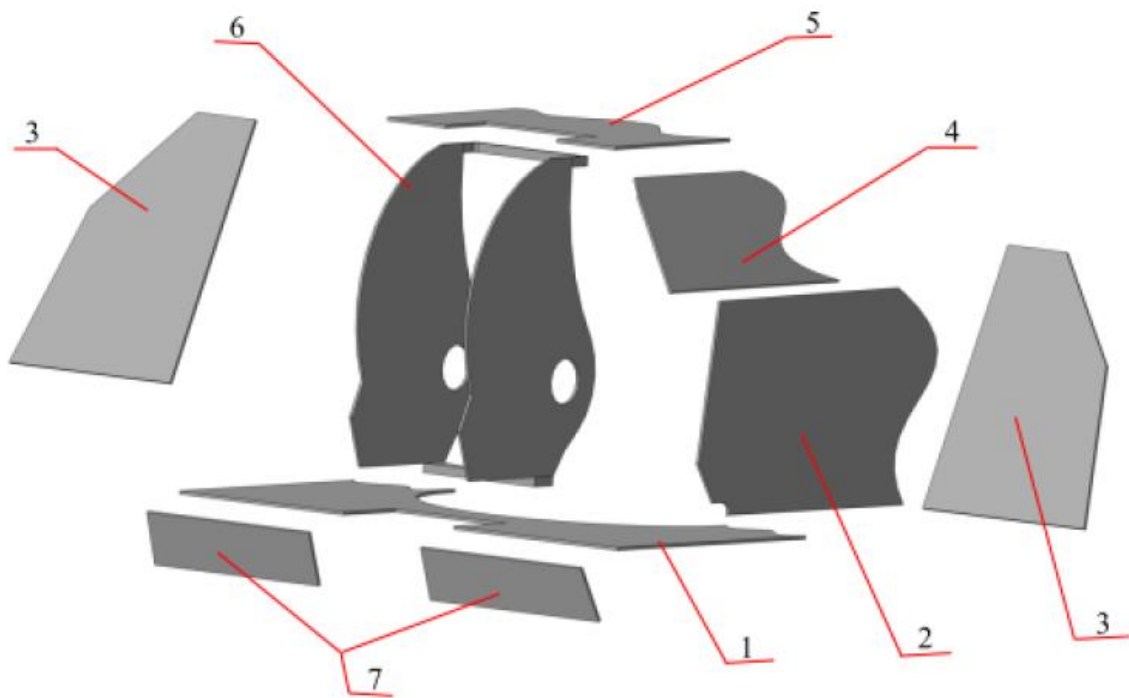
Деталювання при складанні корпусу: 1 – нижній лист; 2 – нижній лист борту; 3 – верхній лобовий лист; 4 – верхній листок борту; 5 – стельовий лист; 6 – верстат ; 7 – нижній лист.
